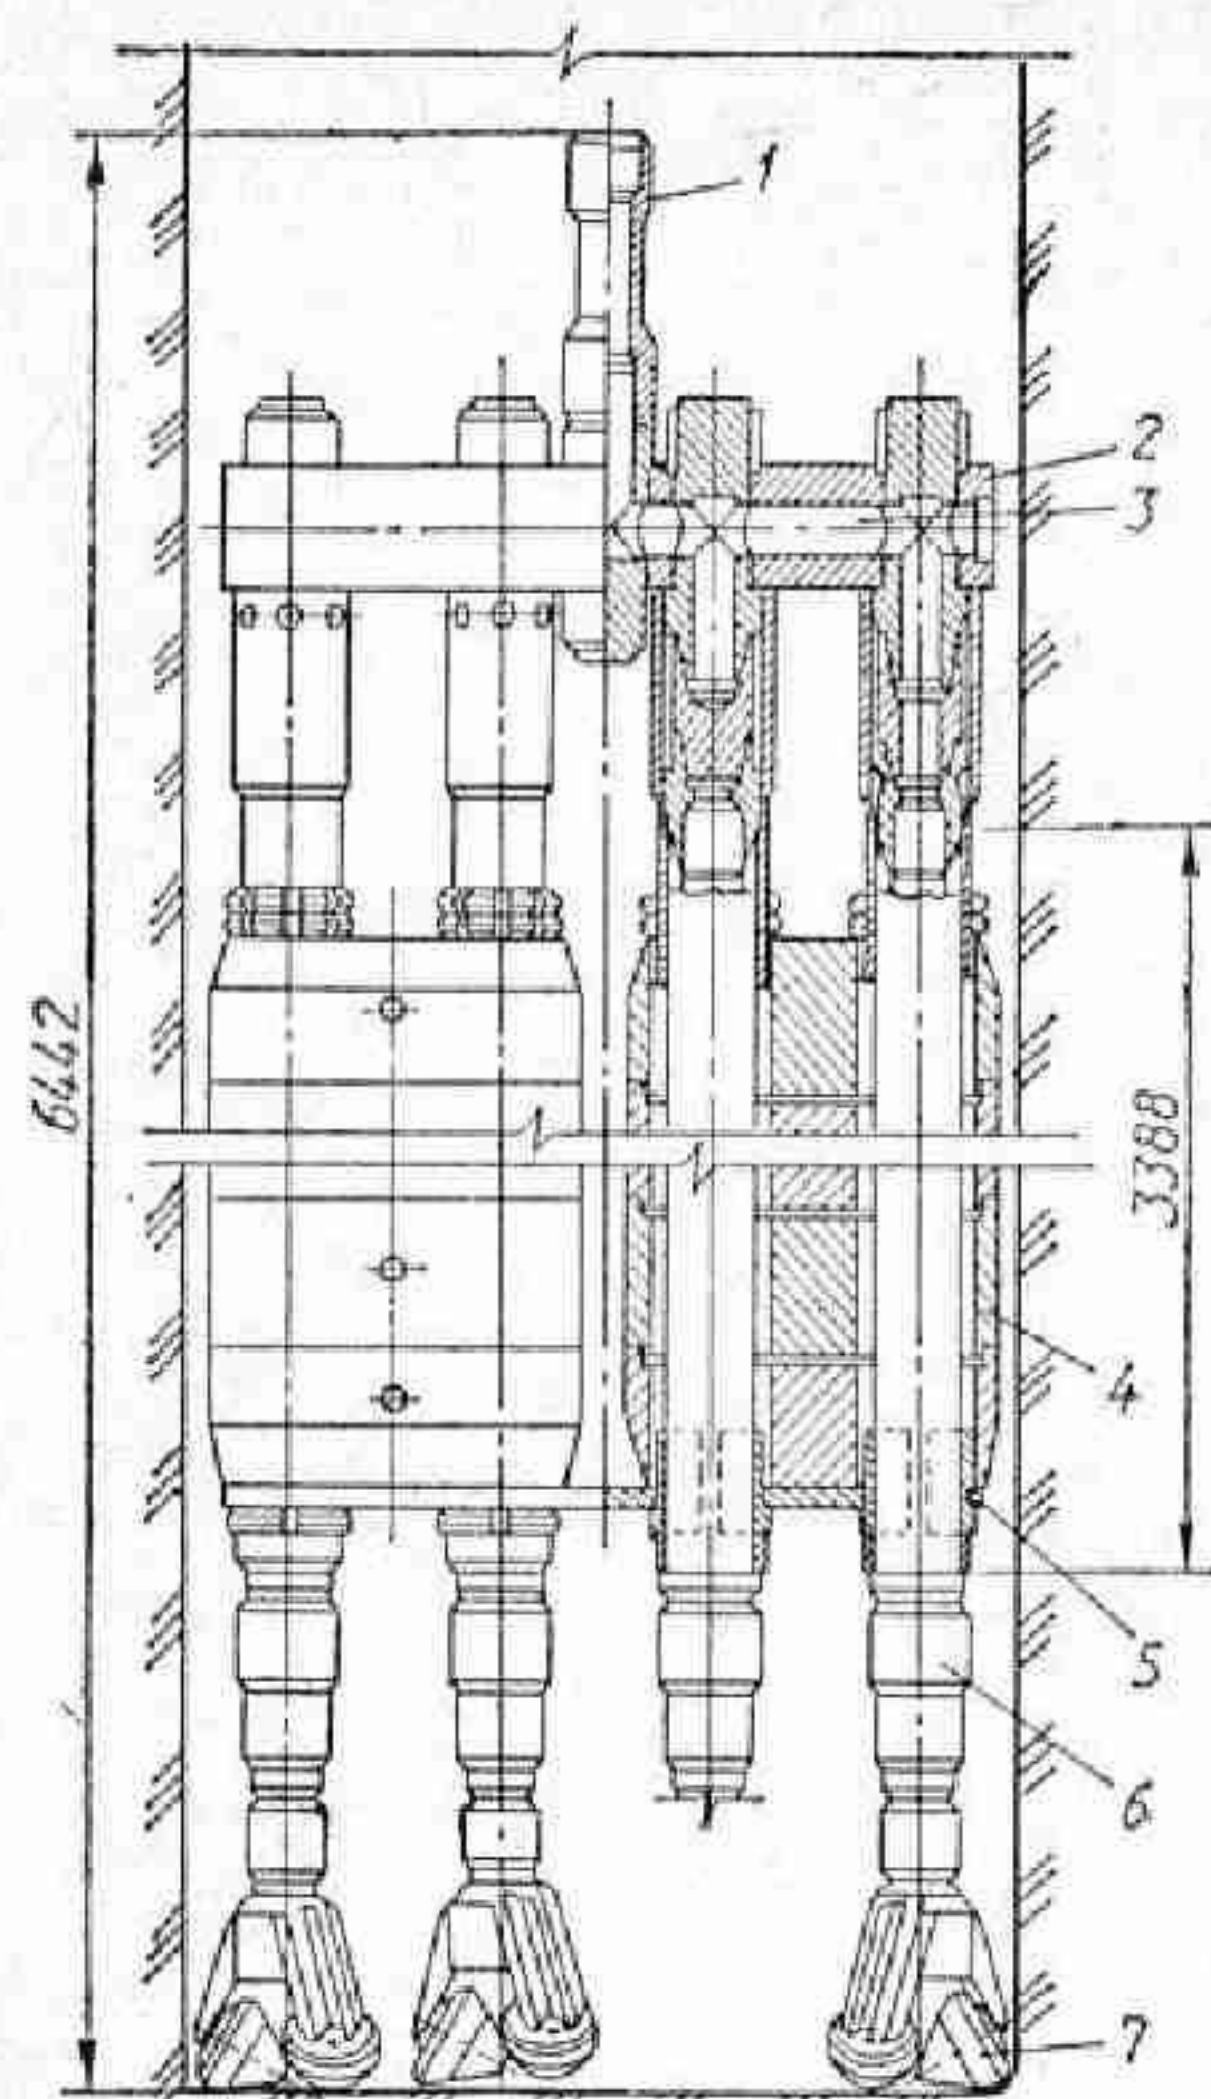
Реактивно-турбинный агрегат РТА:
